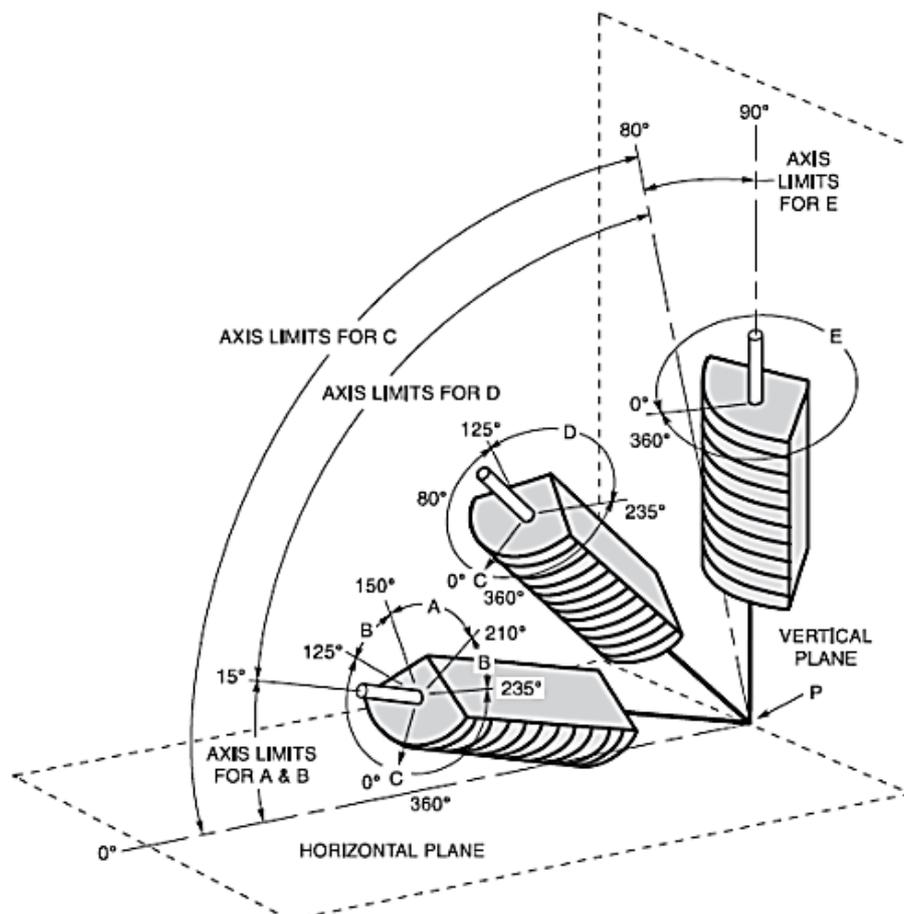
Esquema de posiciones de soldadura en Filete.
